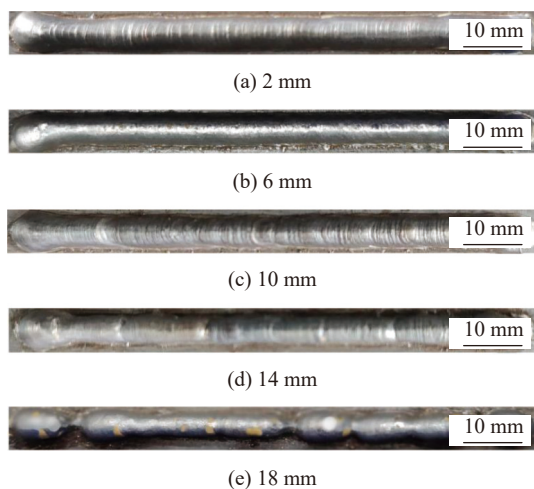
不同焊丝伸出长度下的焊缝形貌
